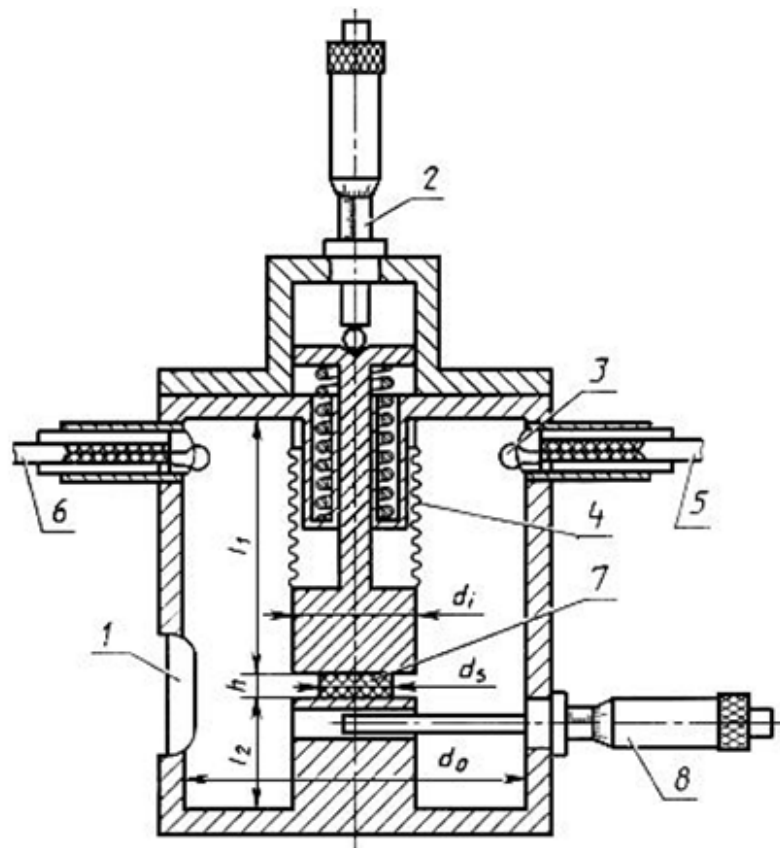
Коаксиальный измерительный резонатор по стандарту МЭК [11]
